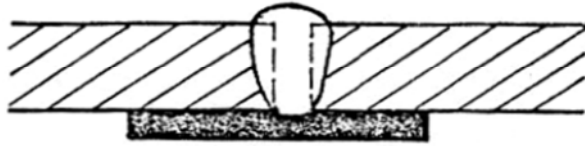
Soudure autogène bout à bout sur chanfrein en V
